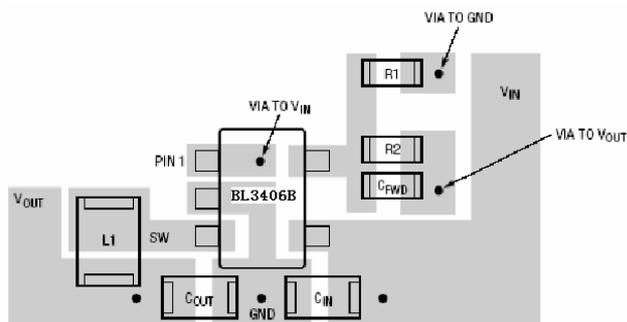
Buck 开关式 DC/DC 应用 PCB 设计
